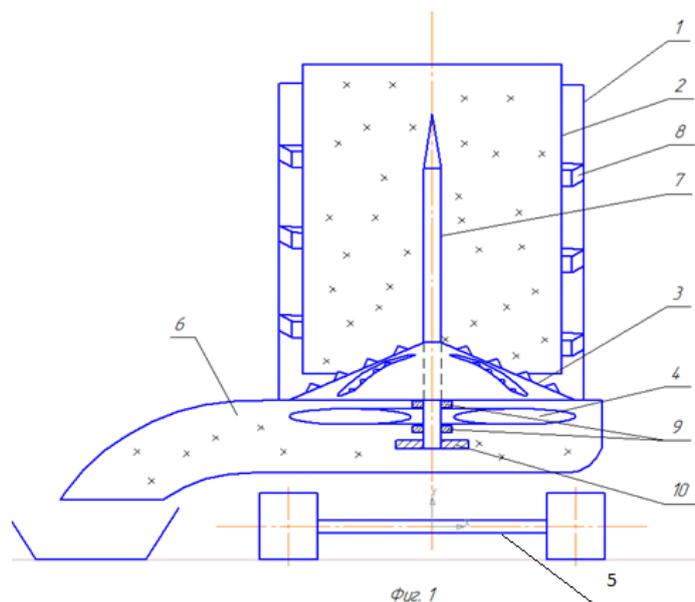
Конструктивно-технологическая схема измельчителя грубых кормов: 1 - бункер; 2 – рулон; 3 - измельчающий рабочий орган конусного типа; 4 - лопастное колесо; 5 - ходовая часть; 6 - воздуховодом; 7 - игла; 8 - шнековая навивка; 9 - подшипник; 10 - привод шкива
